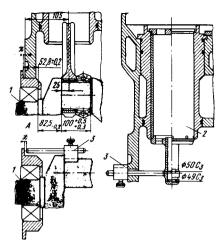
Приспособление для определения толщины прокладки между фланцем корпуса подшипника и фланцем передней стенки картера:
